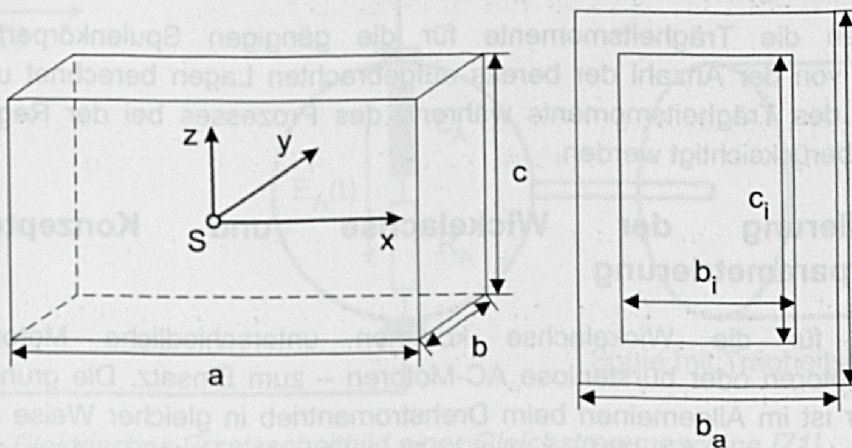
Bezeichnungen am Spulenkörper mit rechteckigem Querschnitt
